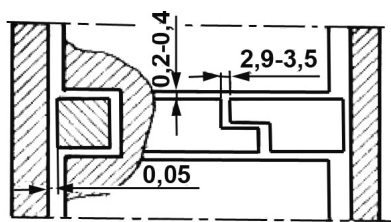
Величина зазоров в поршневой камере предохранительного клапана промежуточного перегрева
